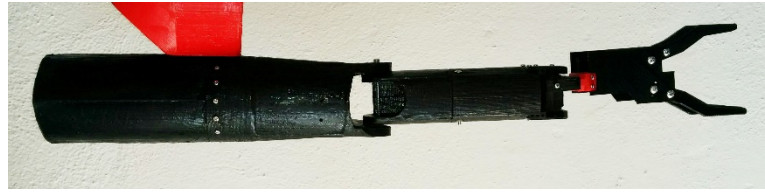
Montaje final del prototipo del brazo robot. I.P.
